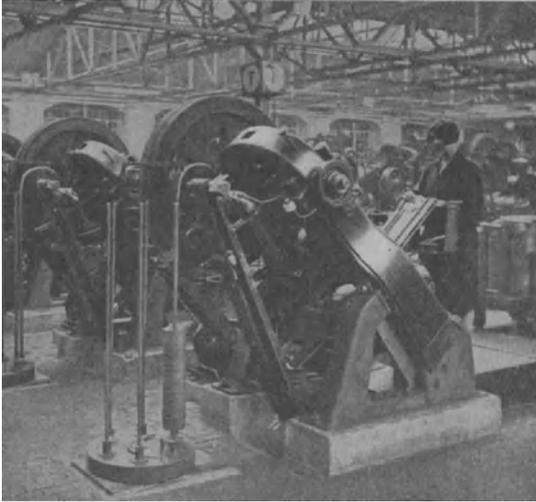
Presse, eingerichtet für wirtschaftliche Fertigung. (Aus Maschinenbau 1927 S. 1125.)
